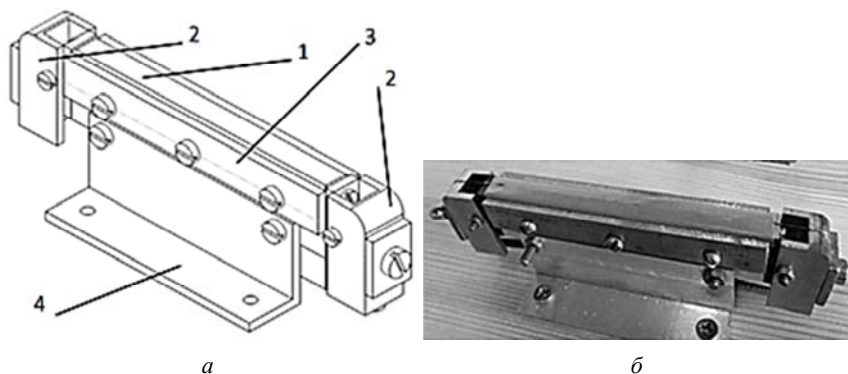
Трехмерное изображение сварочной головки (*а*) и фотография ее общего вида (*б*):
